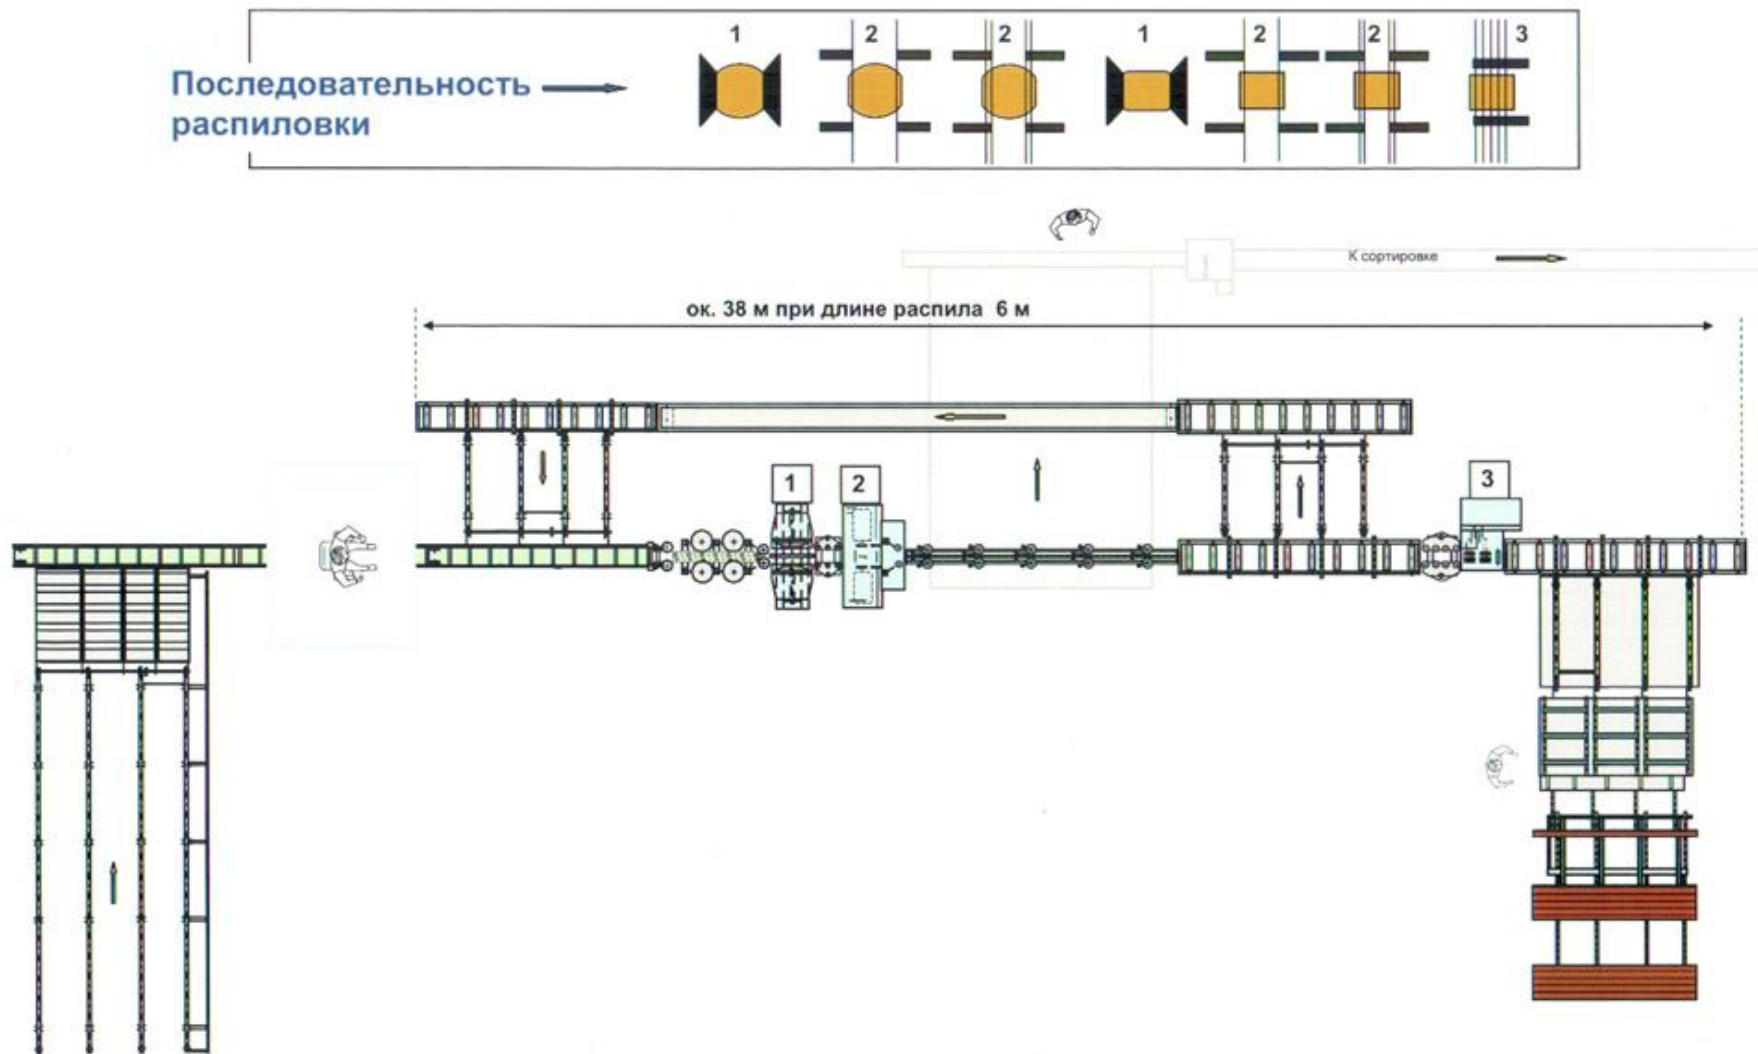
Фрезерно-брусующая установка с круговой подачей сортиментов с двухшпиндельным многопильным делительным круглопильным станком для раскря бруса, производительностью 35-110 тыс. м³ бревен в год /9/
